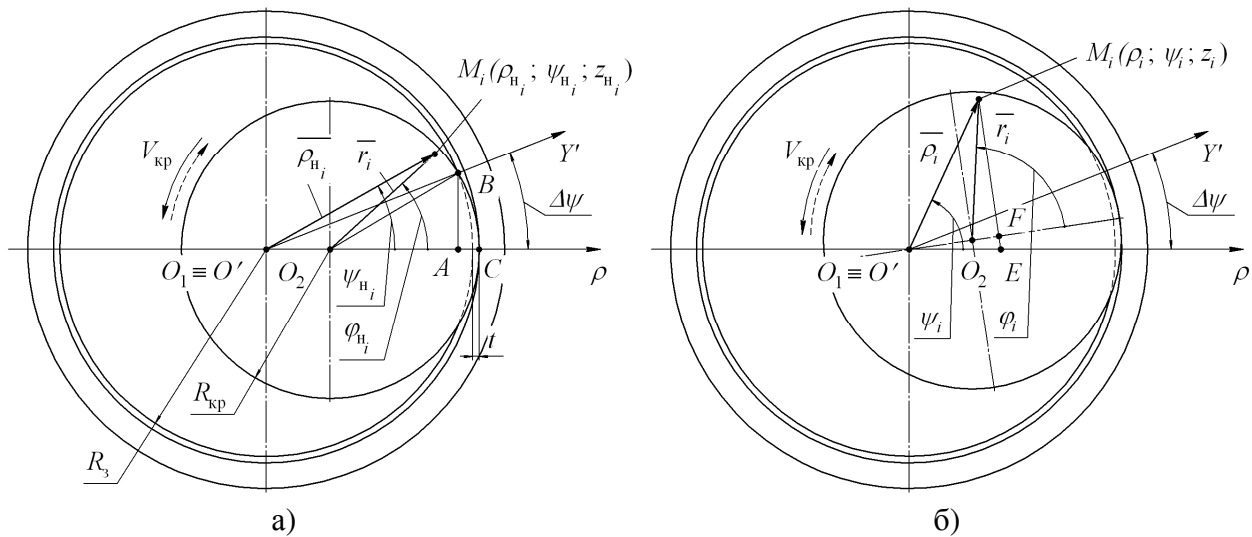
Положение ШК и заготовки при внутреннем круглом шлифовании (вид спереди):
